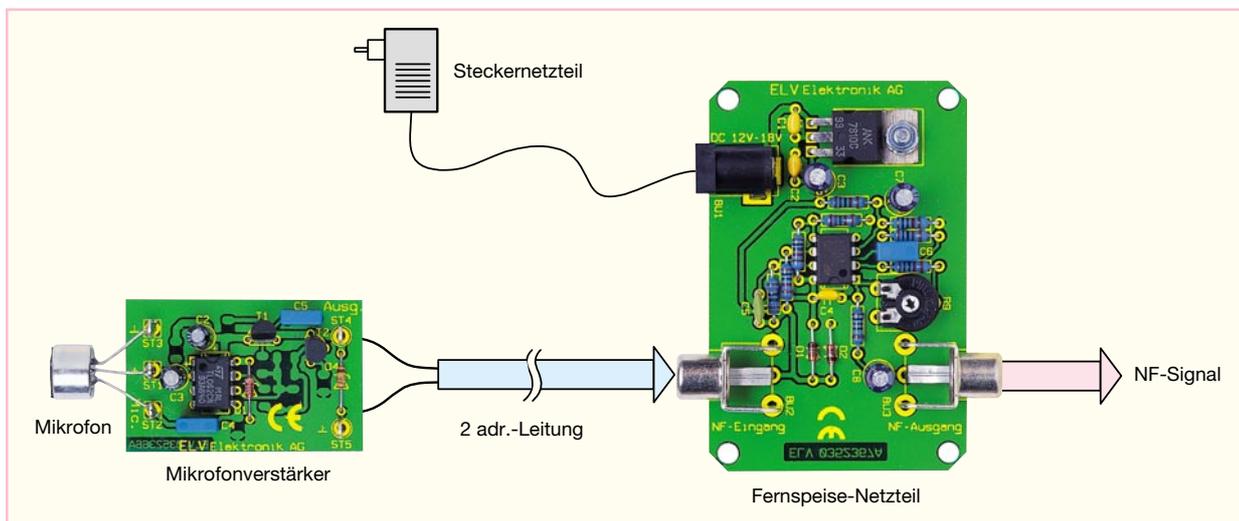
Das Anschlussschema für die Verkabelung aller Komponenten
